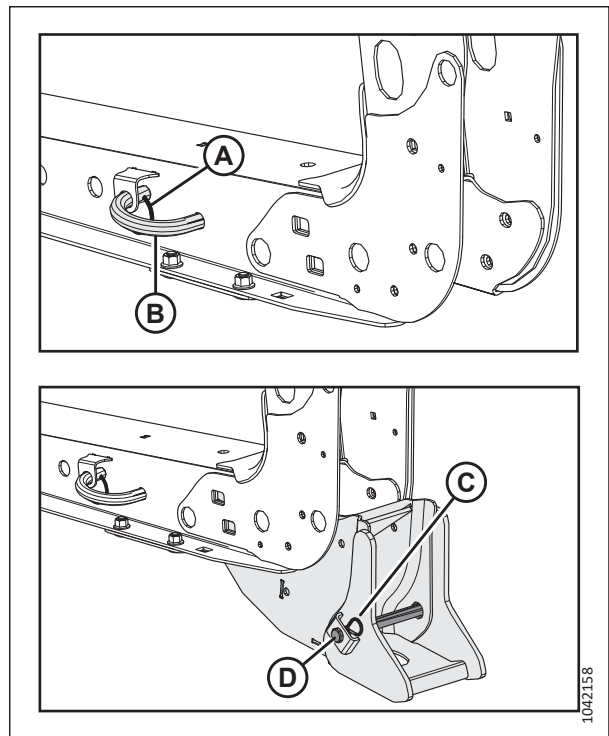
Étauçon de la plateforme de coupe – Côté gauche illustré
